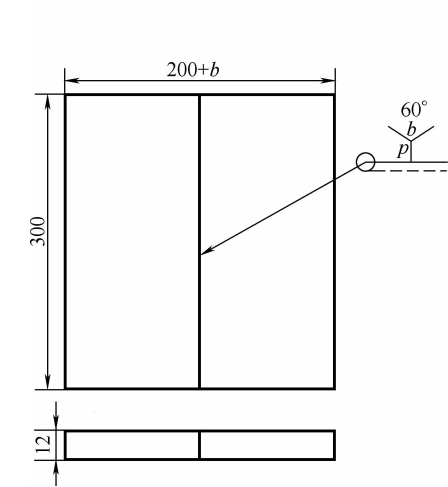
平板件 V 形坡口对接 CO₂ 气体保护焊装配图
